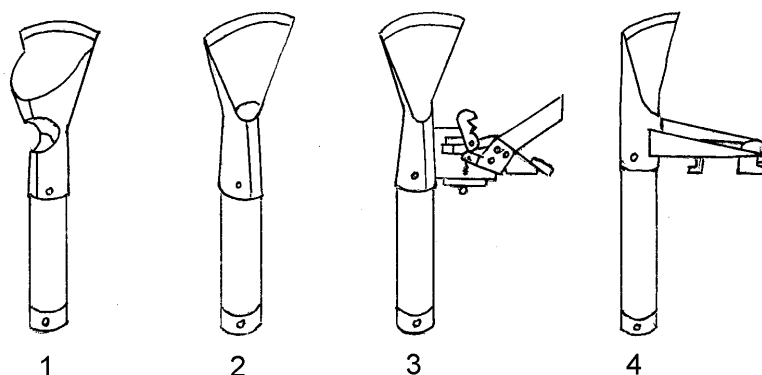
Инструменты для изготовления щапа и установки приемников:
